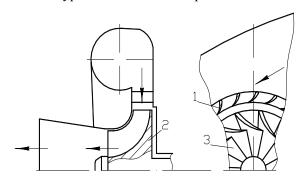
Схема центростремительной турбины: 1 – решётка неподвижных лопаток; 2 – диск; 3 – решётка рабочих лопаток
